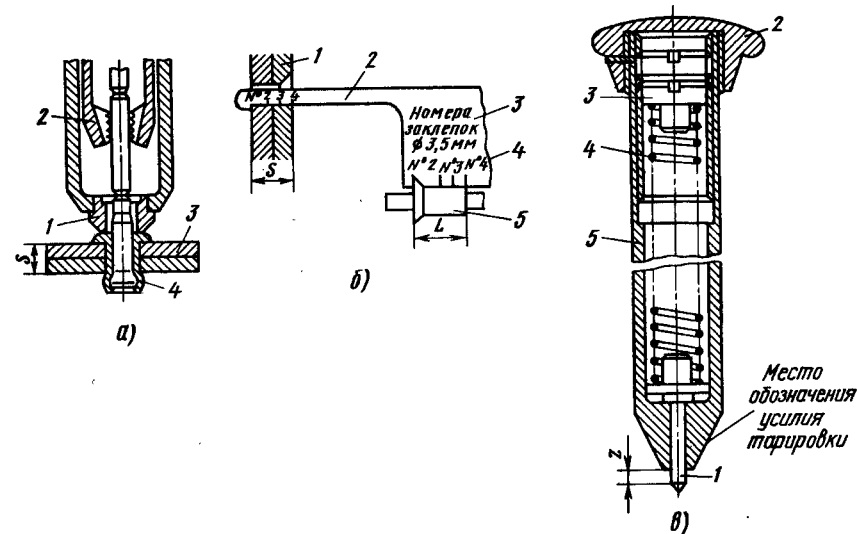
Инструмент для установки и контроля заклепок с сердечником: а - для установки заклепки с сердечником: 1 - наконечник; 2 - захват пресса; 3 - соединяемые детали; 4 - заклепка; б - для контроля соответствия длины заклепки пакету: 1 - пакет; 2 - шкала номера заклепки; 3 - шаблон; 4 - шкала длины заклепки; 5 - корпус заклепки; в - динамометр для контроля прочности установки сердечника: 1 - шуп; 2 - рукоятка; 3 - тарировочный винт; 4 - пружина; 5 - корпус
